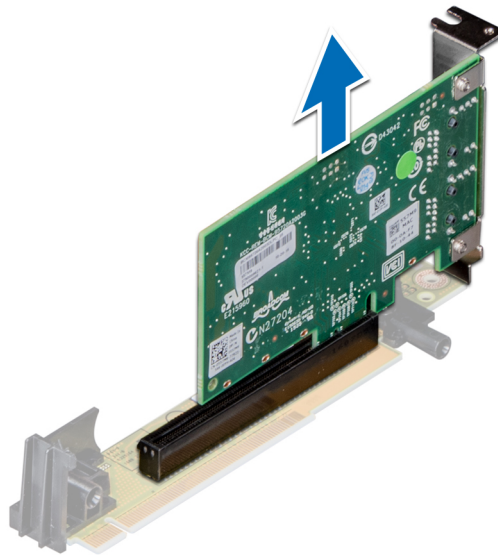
Retrait de la carte d'extension de la carte de montage 2
